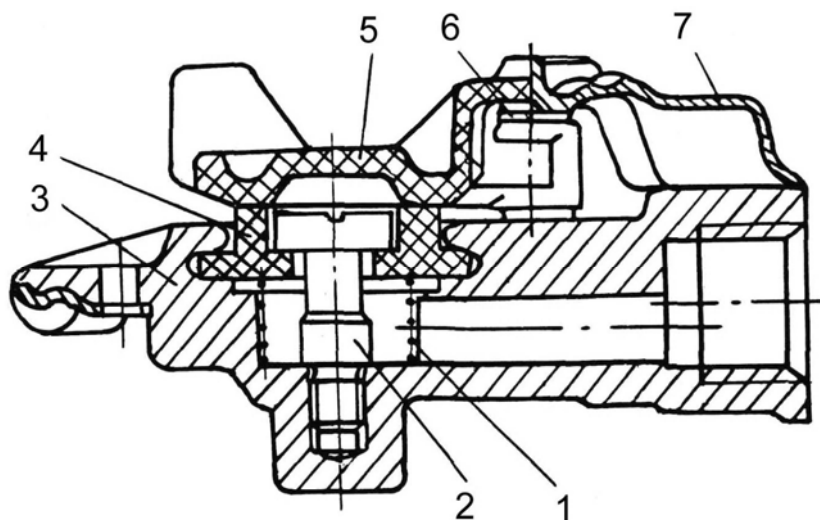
Головка соединительная типа «Палм»: 1-пружина; 2-клапан; 3-корпус; 4-уплотнитель; 5-крышка; 6-ось крышки; 7-крышка корпуса
